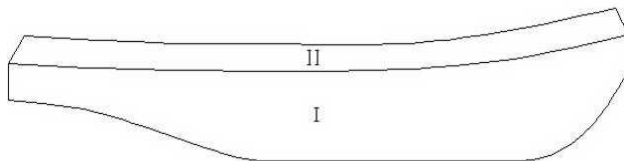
Наружная обшивка основного корпуса и фальшборта.
